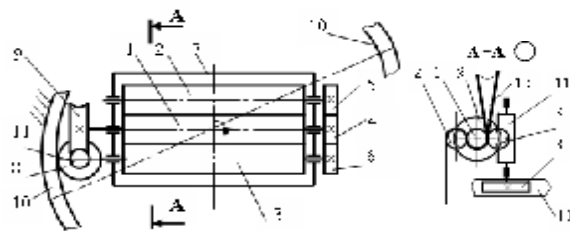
Кінематична схема механізму відтяжки полотна: 1–3 – відтяжні валики; 4–6 – циліндричні шестерні; 7 – рама; 8 – шестерня; 9 – черв'ячне колесо; 10 – зубчасте колесо; 11 – черв'як; 12 – трикотажне полотно
